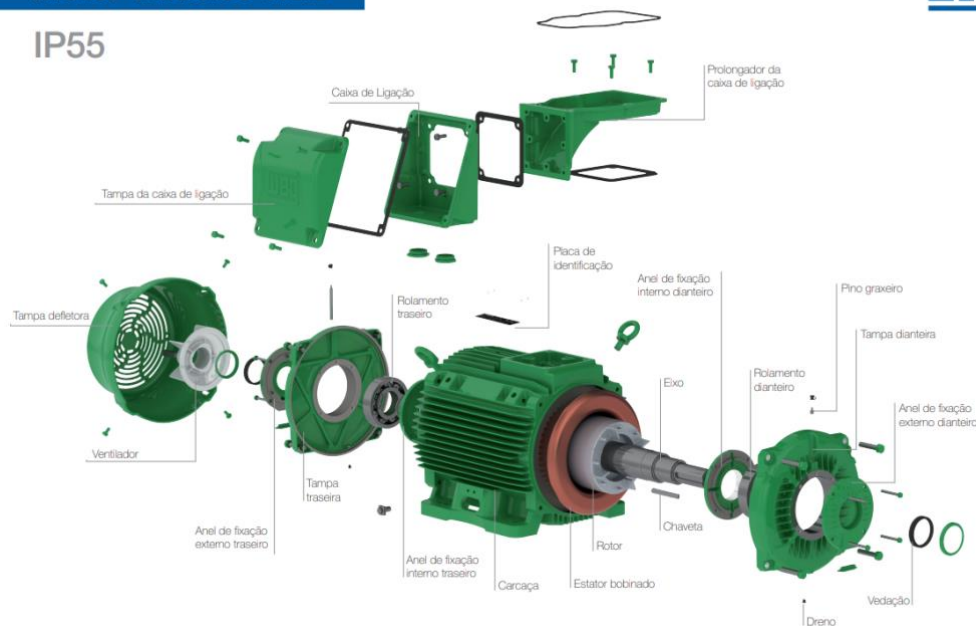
Vista explodida de um motor trifásico de indução fonte: WEG
